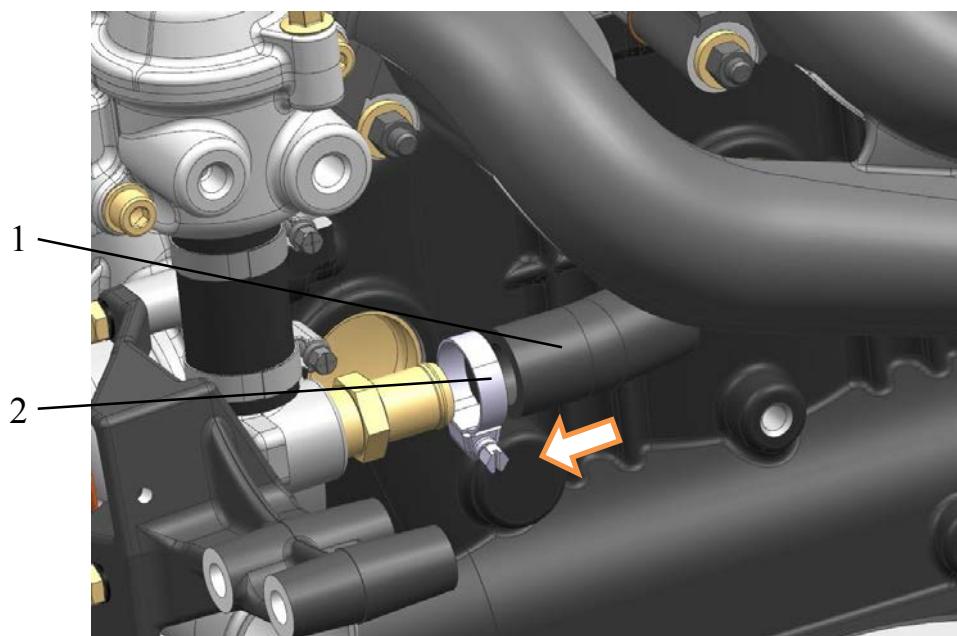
Установка шланга трубки забора охлаждающей жидкости:
